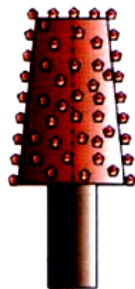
Конструкция инструмента, изготовленного методом порошковой металлургии
